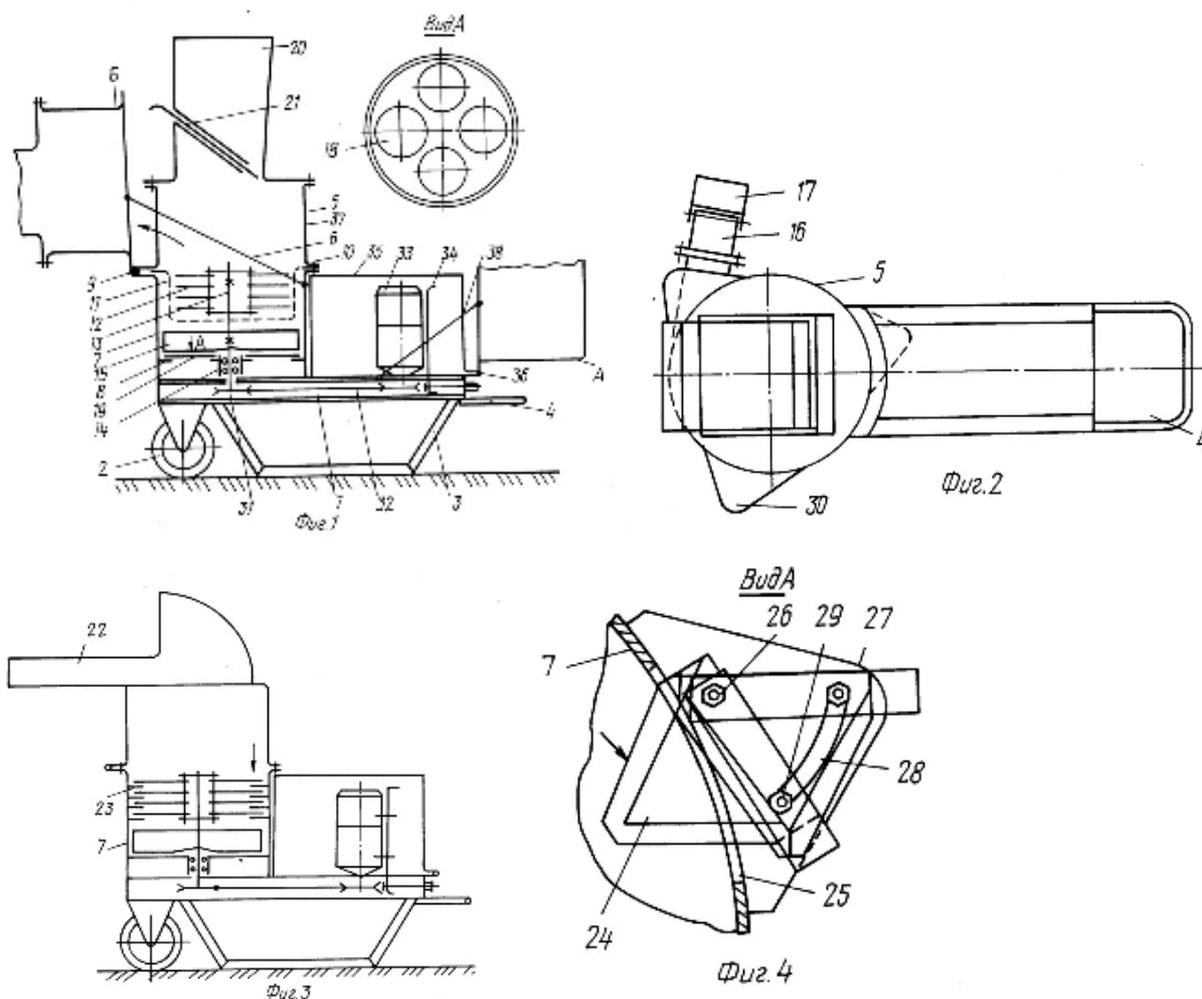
Малогабаритный фермерский измельчитель - смеситель кормов
